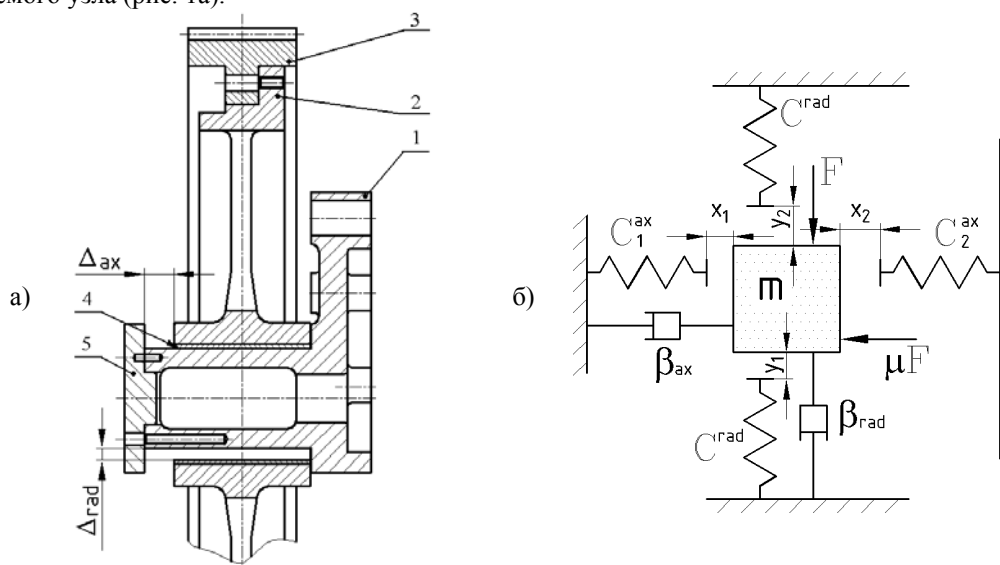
Поперечный разрез (а) и динамическая схема (б) промежуточной шестерни привода ТНВД
